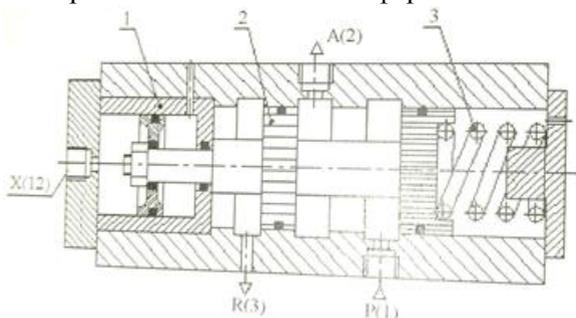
Золотниковый 3/2 распределитель с пневмоуправлением
